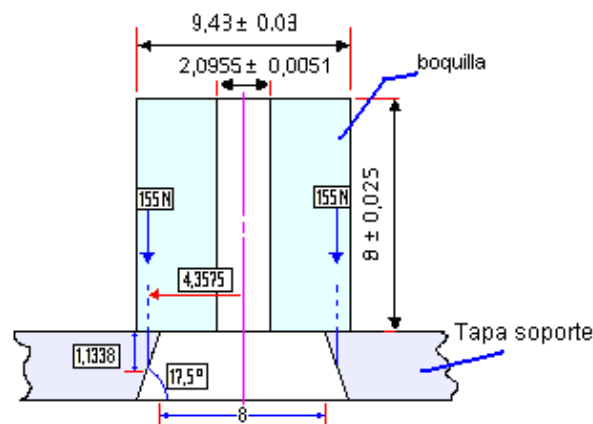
Esquema de la zona de contacto entre la tapa soporte del cilindro y la boquilla.
